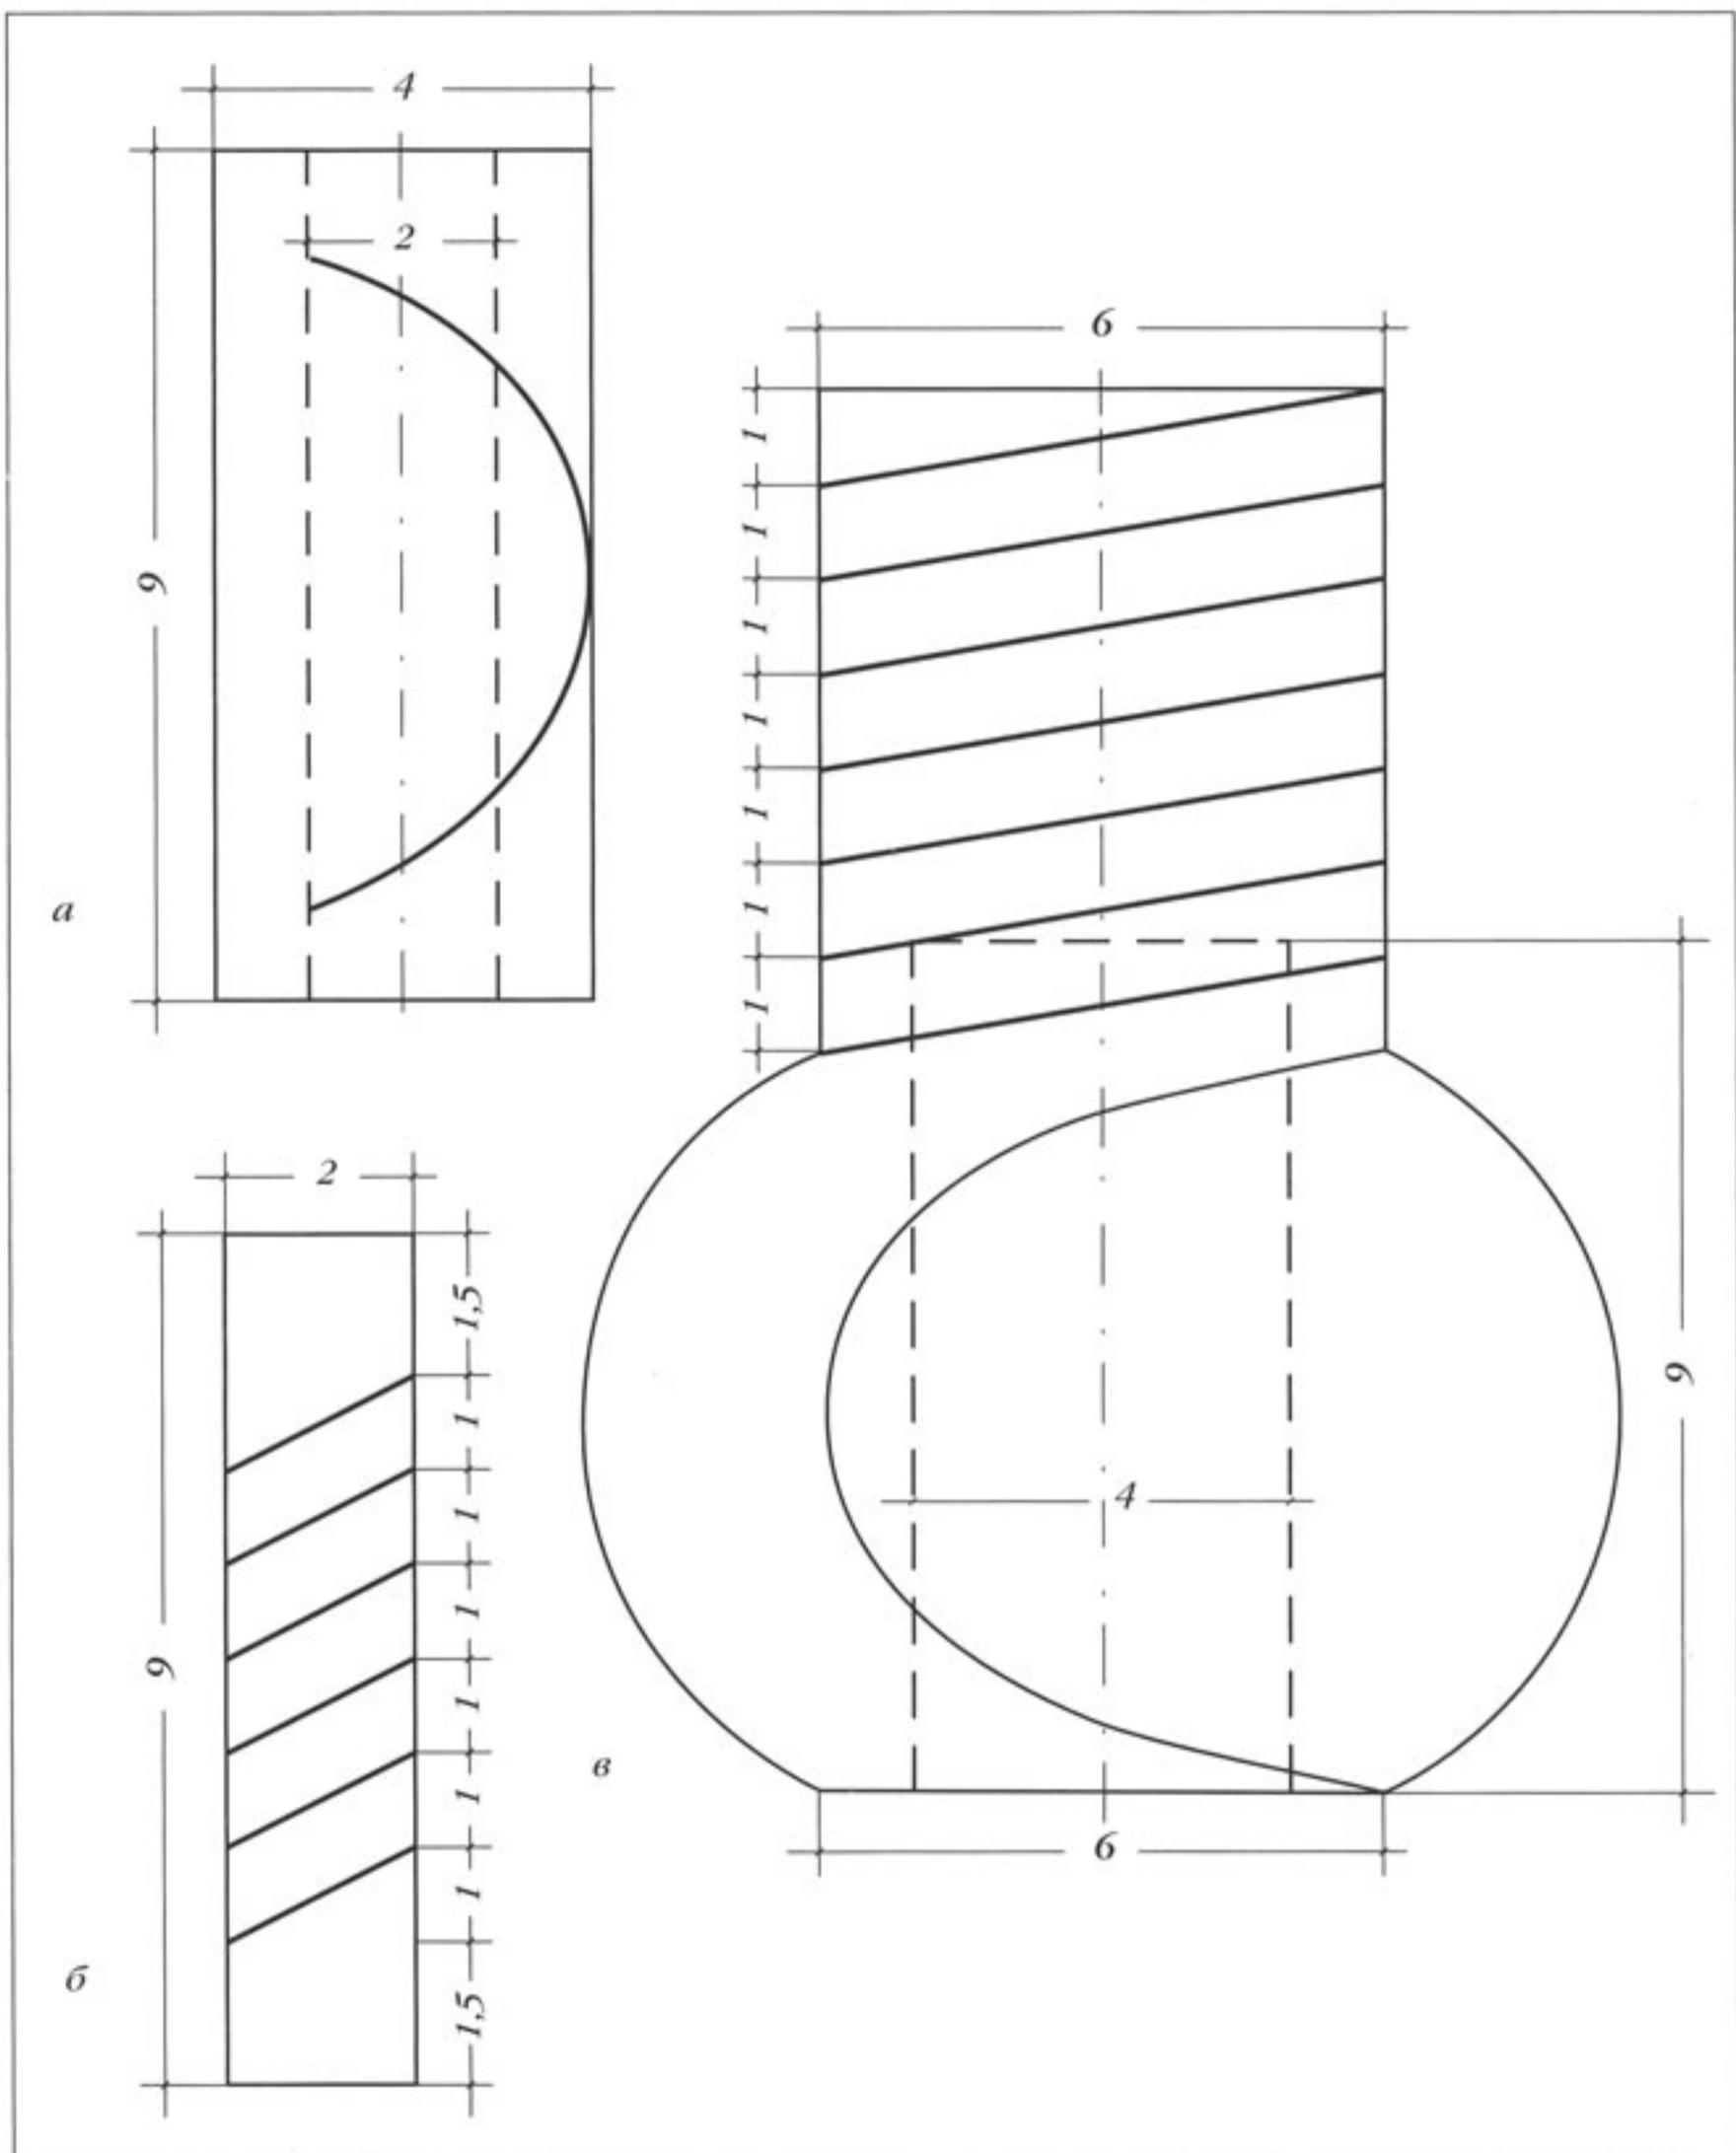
Чертеж и схема разметки деталей стойки чаши-вазы к рис. 192: а – внутренняя деталь (трехзаходный вариационный винт); б – внутренняя деталь (четырехзаходный винт, шаг 1); в – наружная деталь (верхняя часть – шестизаходный винт, шаг 1; нижняя – вариационный винт, шаг 1)
